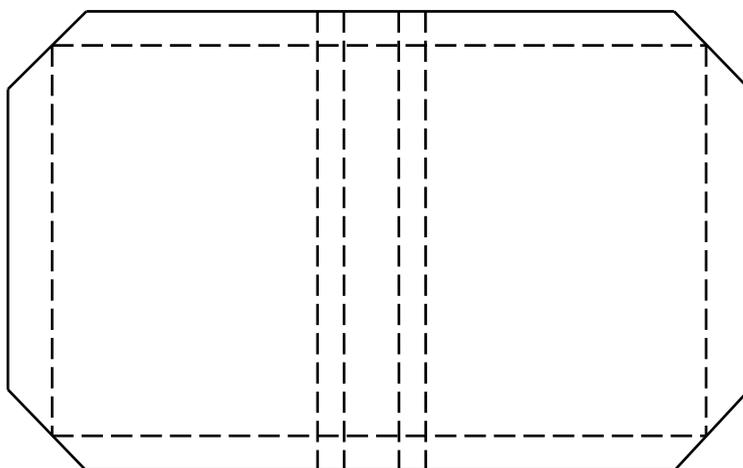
Вид заготовки для интегральной переплетной крышки
